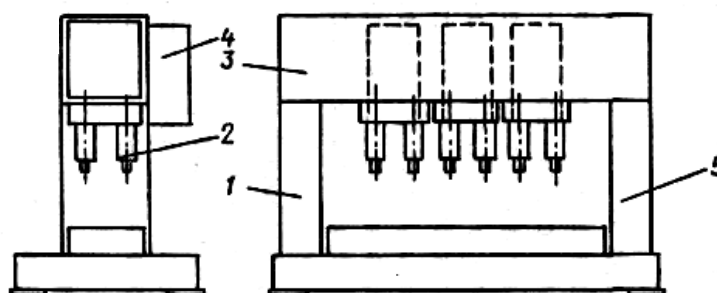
Многоэлектродная контактная сварочная машина на базе порталного двухстоечного пресса
